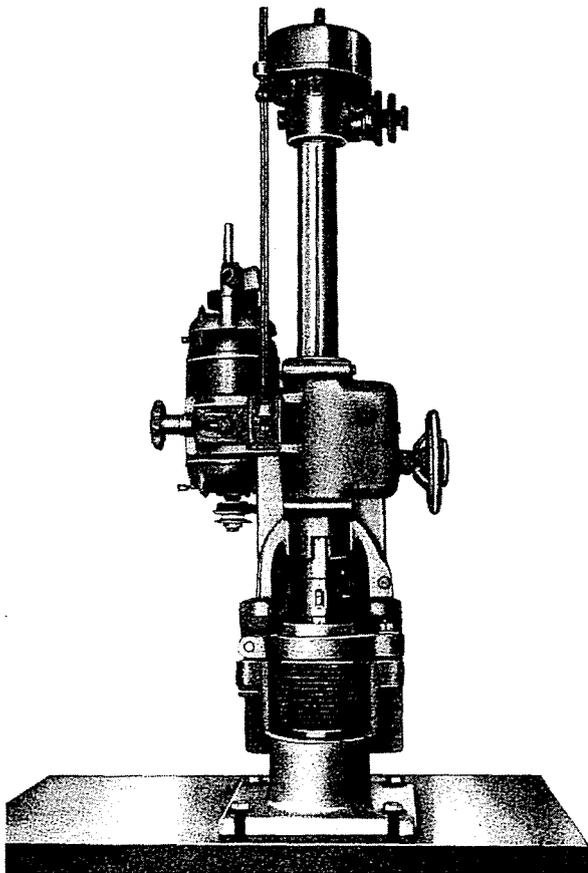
Ausbohren eines mit Werkzeug A. 60000 aufgespannten Zylinders mit der tragbaren Bohrmaschine M. 111.
